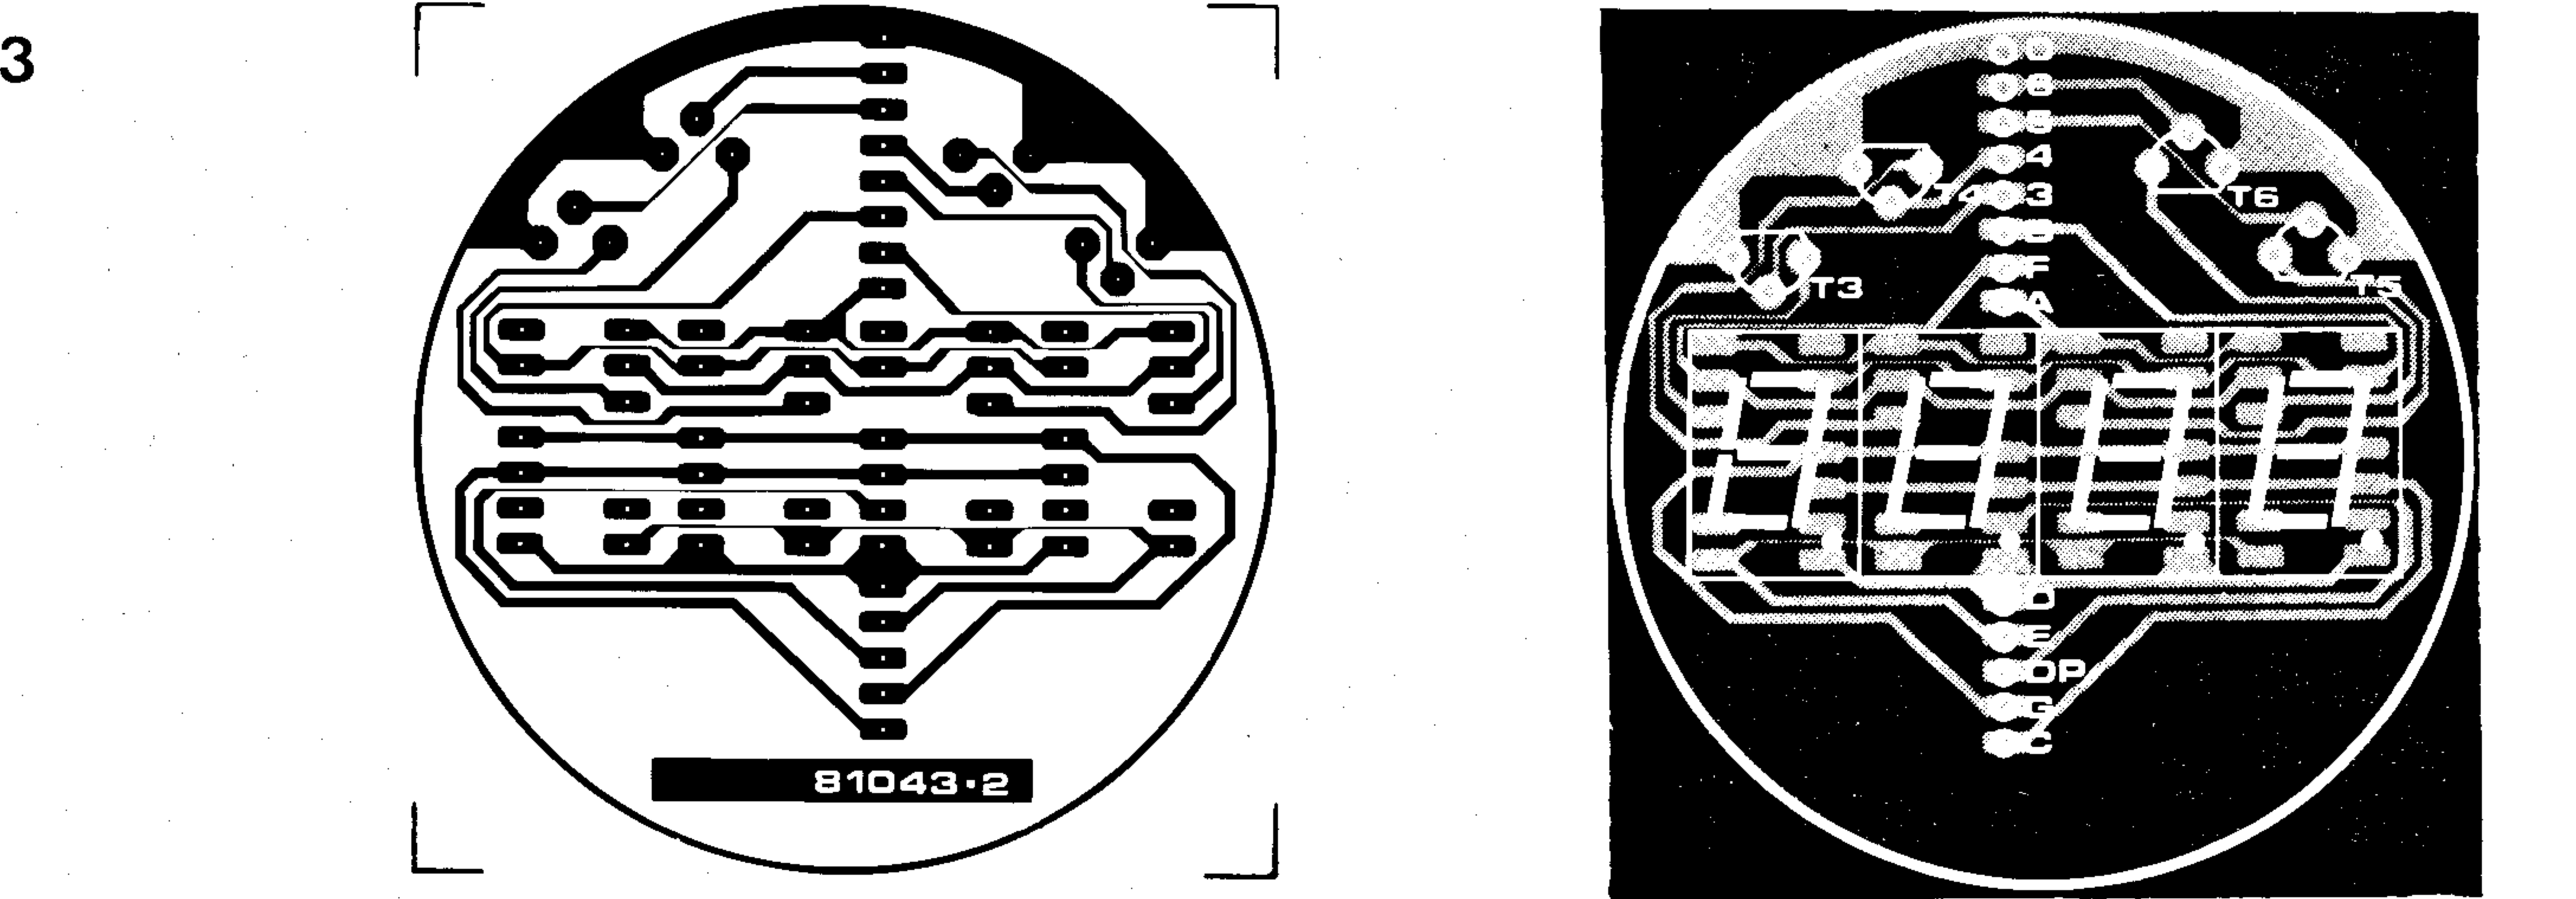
Placa de circuito impreso y disposición de componentes para el visualizador.
